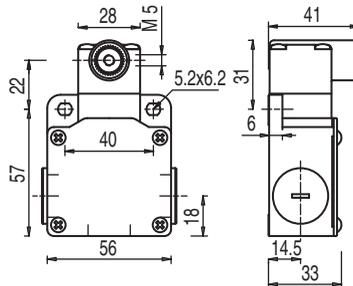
Dimensiones S300-M13C3-M20-SB en mm
